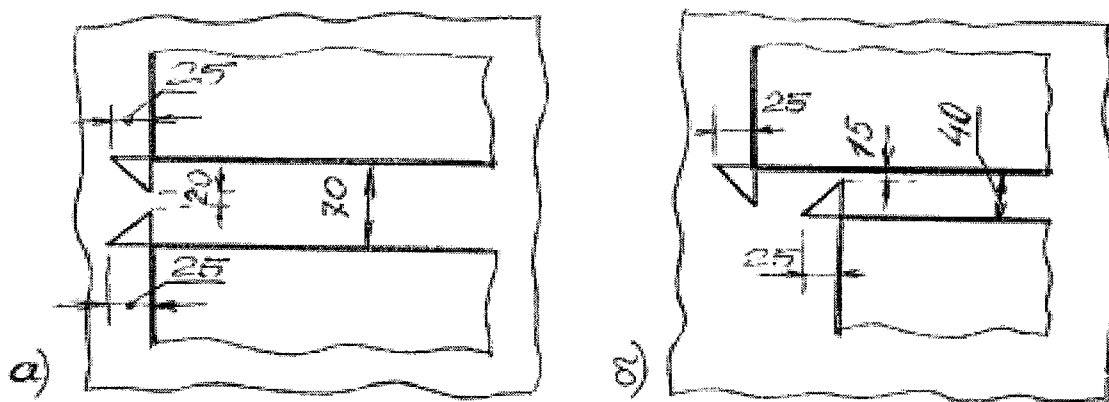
а) ОБРАЗЕЦ, неправильного расположения деталей;
